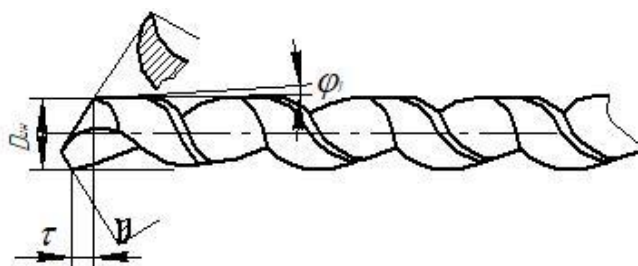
Инструмент для обработки отверстий с обратной конусностью
